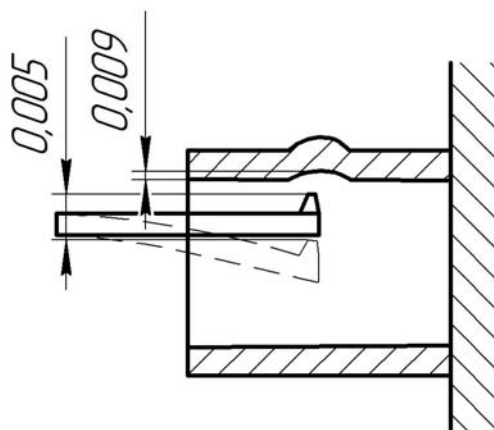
Отжим резца в процессе нарезания резьбы
